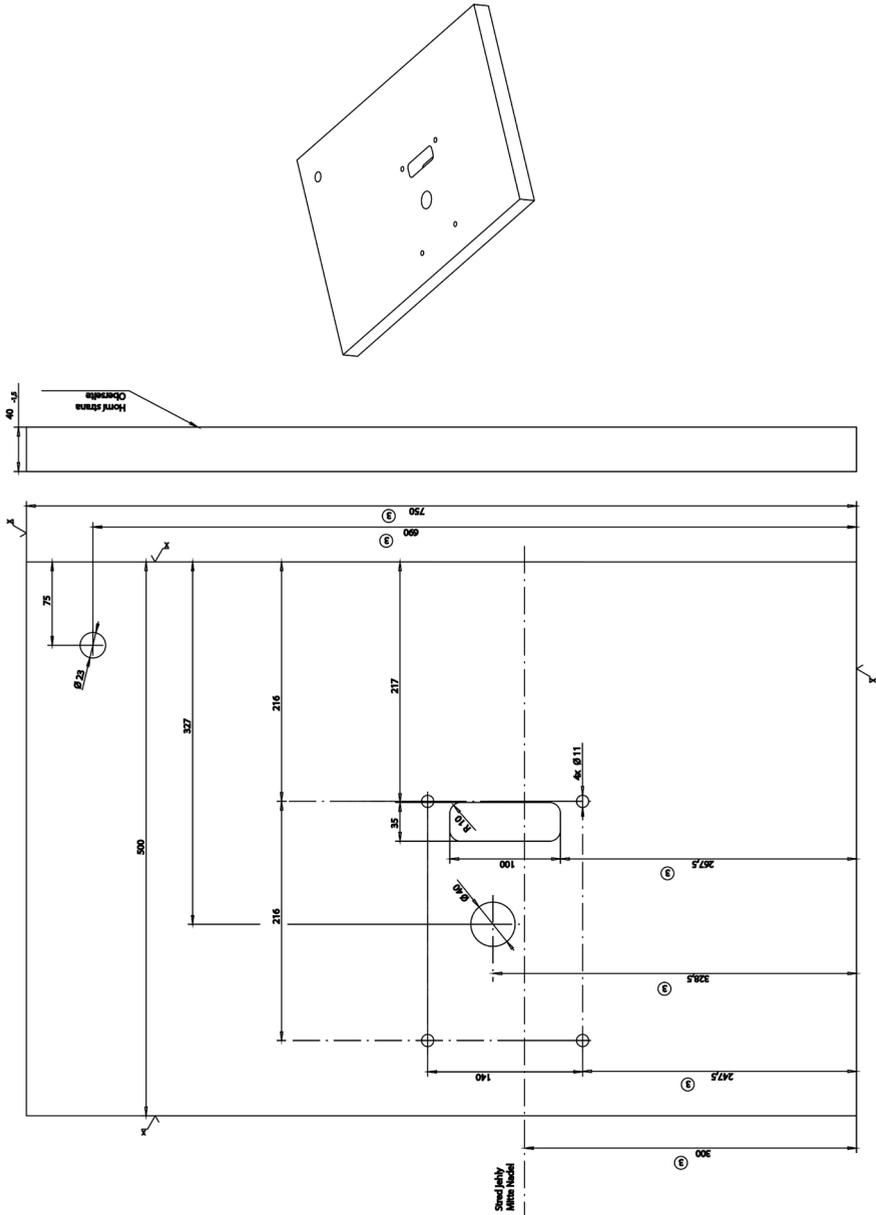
Piano di lavoro fisso, macchine con braccio lungo
